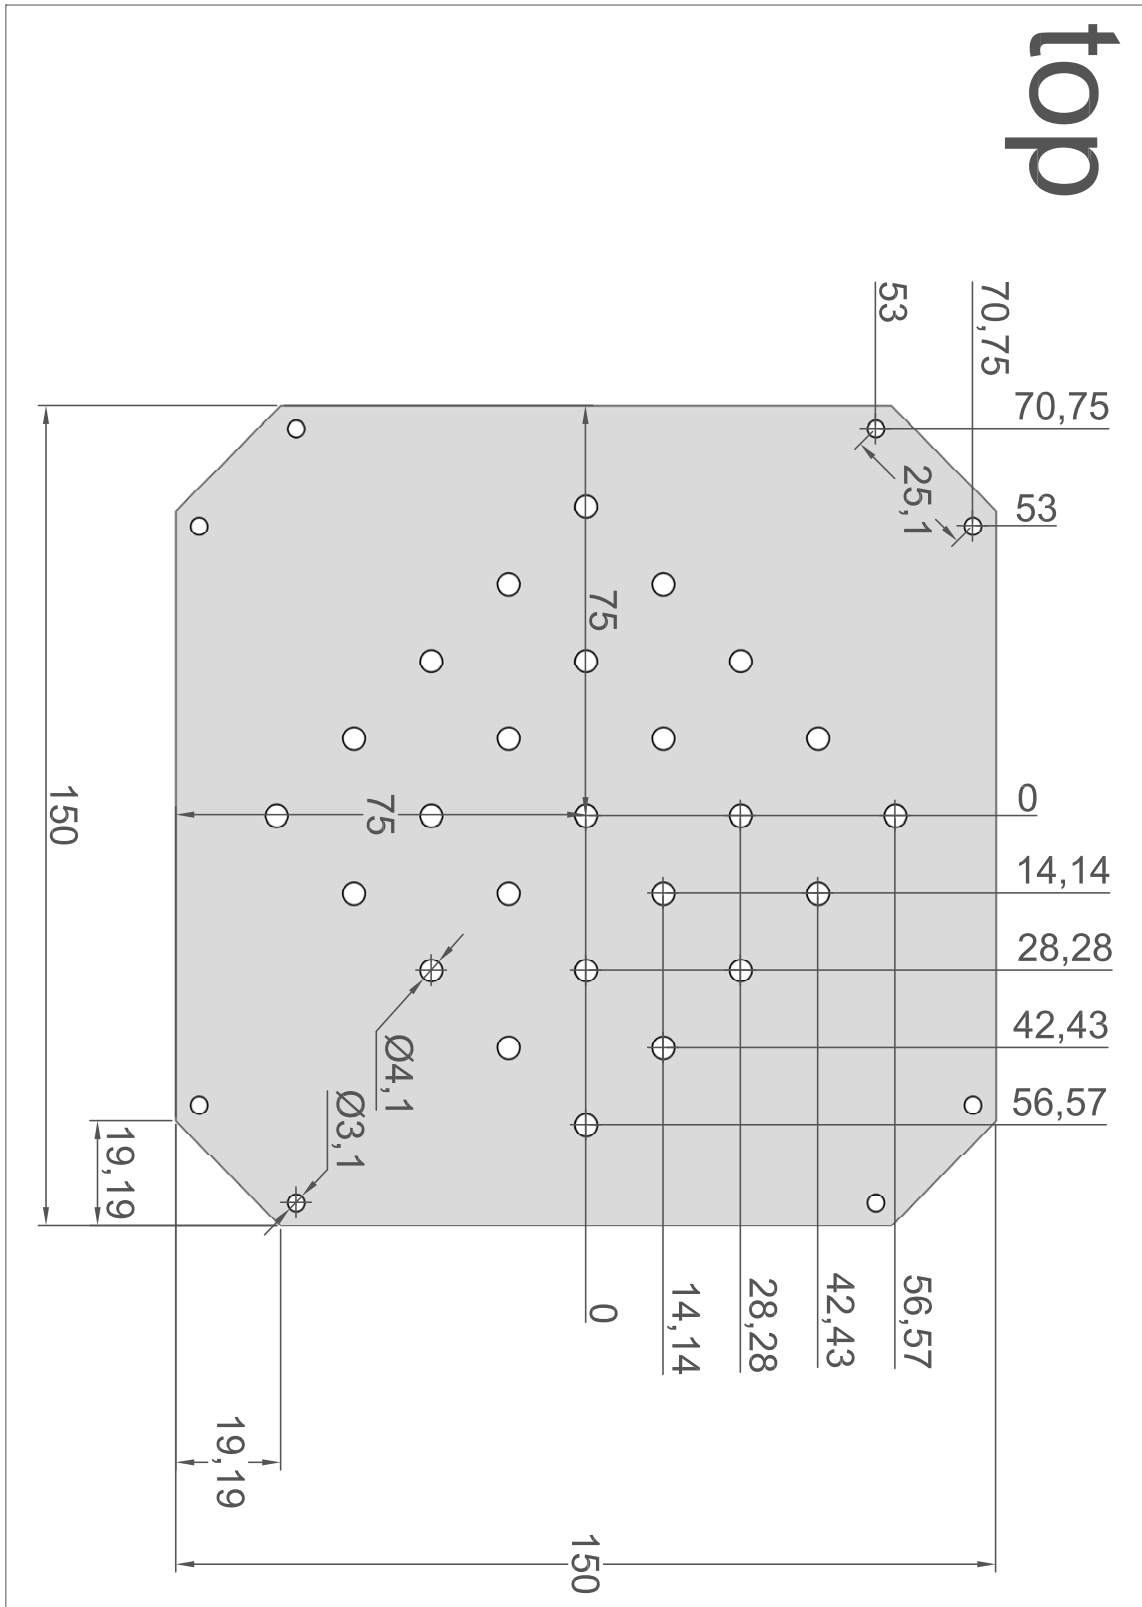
Blaupause der Positionierungsmaske für die Messung des Aufladeeffekts, Aluminium mit 2 mm Materialstärke
